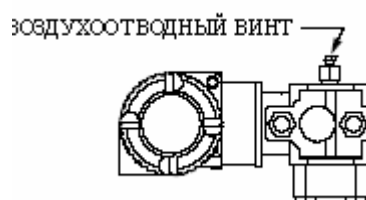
Горизонтальный монтаж - Вентиляция полости
